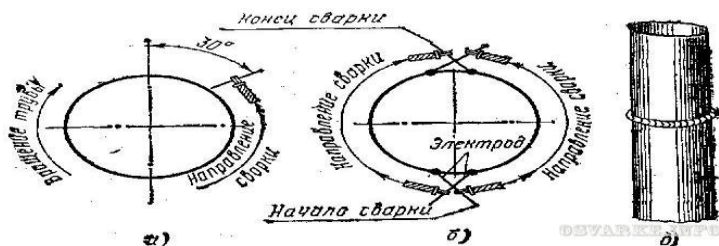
Сварные стыки труб: а – поворотный; б – неповоротный; в – горизонтальный
